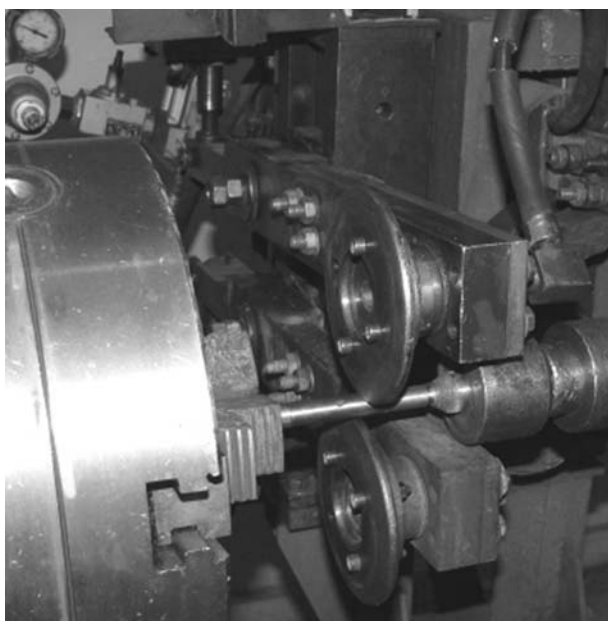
Общий вид узла сварочных клещей с установленными роликами для испытания обкаткой на прочность сцепления
